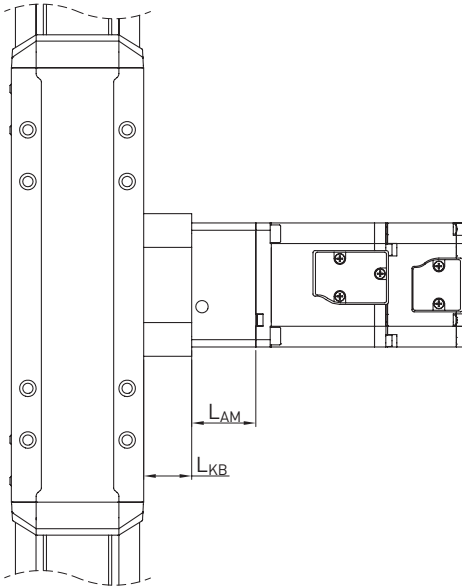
Motoranbindung Auslegerachse HC ohne Getriebe
